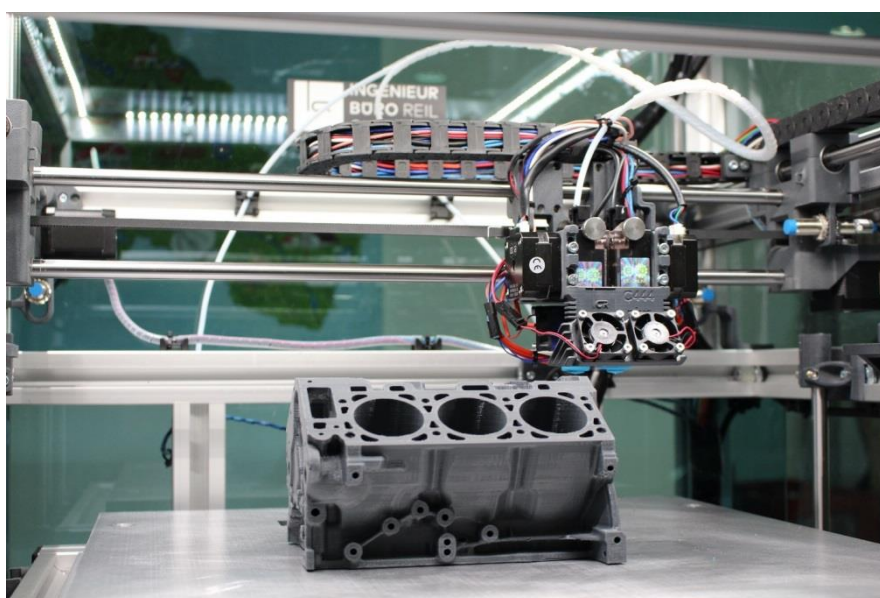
Применение аддитивных технологий для изготовления блока цилиндров двигателя
